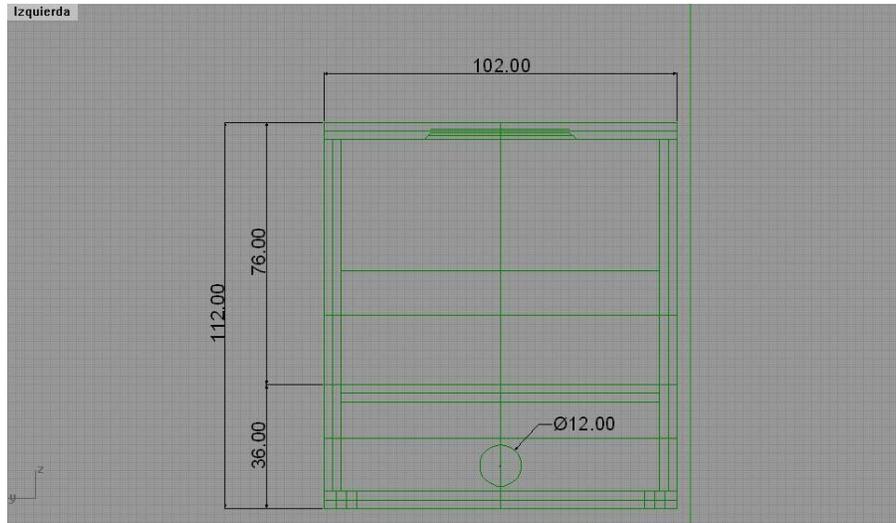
Vista frontal del sistema de aislamiento 1:1 en mm.
